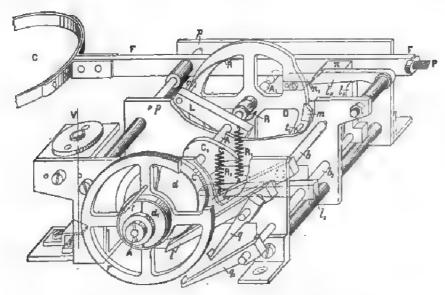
Compteur Meylan-Rechniewski (Détails du mécanisme).
